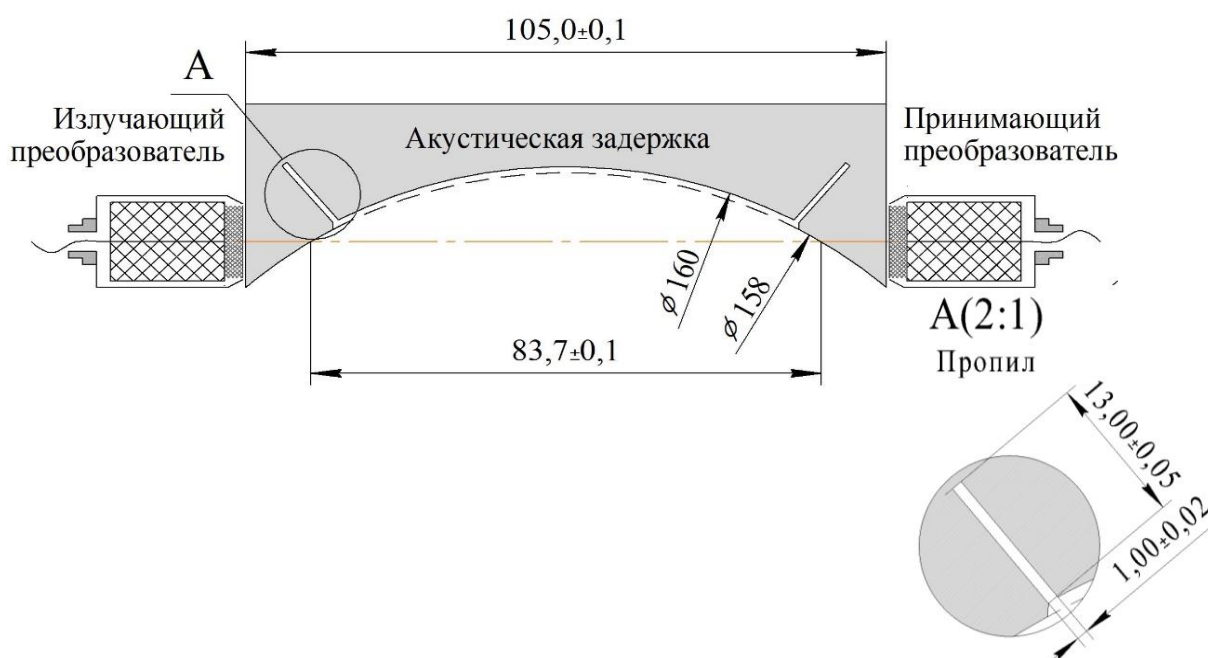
Акустическая задержка с излучающим и принимающим прямыми преобразователями для хордового прозвучивания кольца подшипника продольной волной
